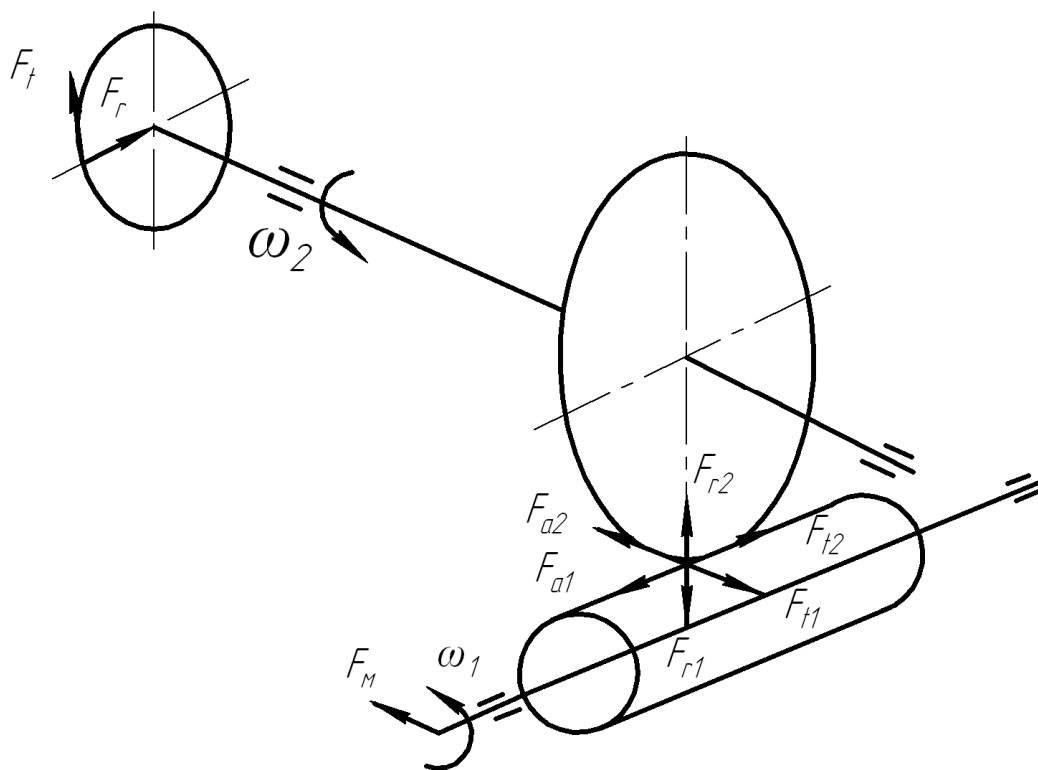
Редуктор червячный с открытой цилиндрической передачей (показана только шестерня ОЗП)
